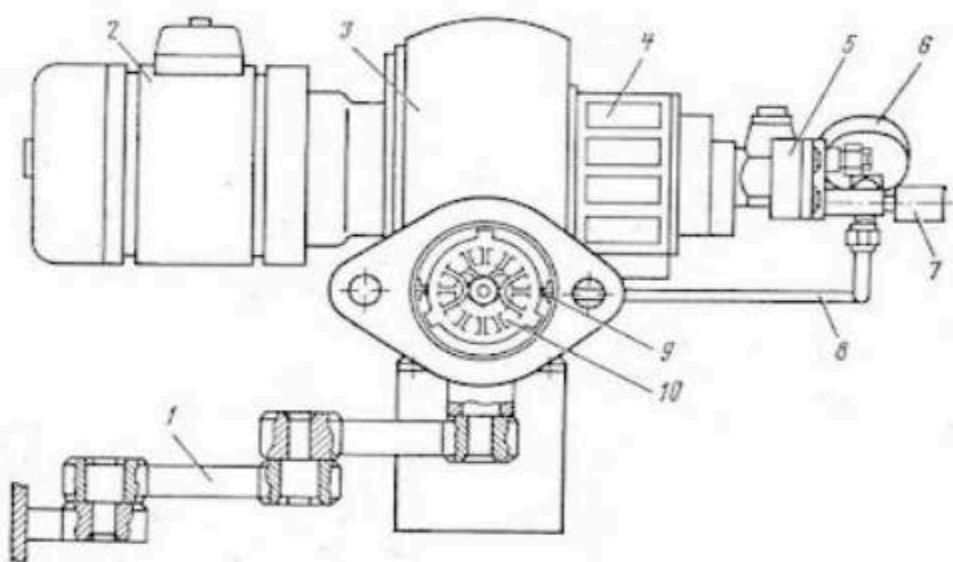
Автоматизированная форсунка АФ65С-220
